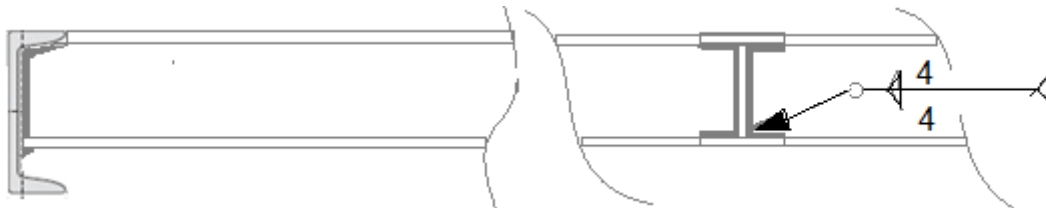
Principais juntas soldadas (Fonte: Elaborado pelos autores)
